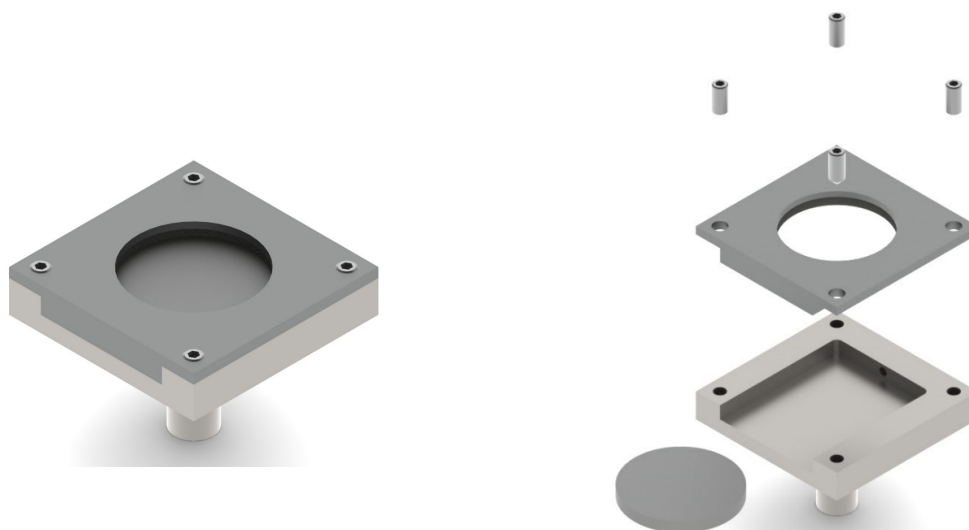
Sistema 5 - vista da montagem e vista explodida.
